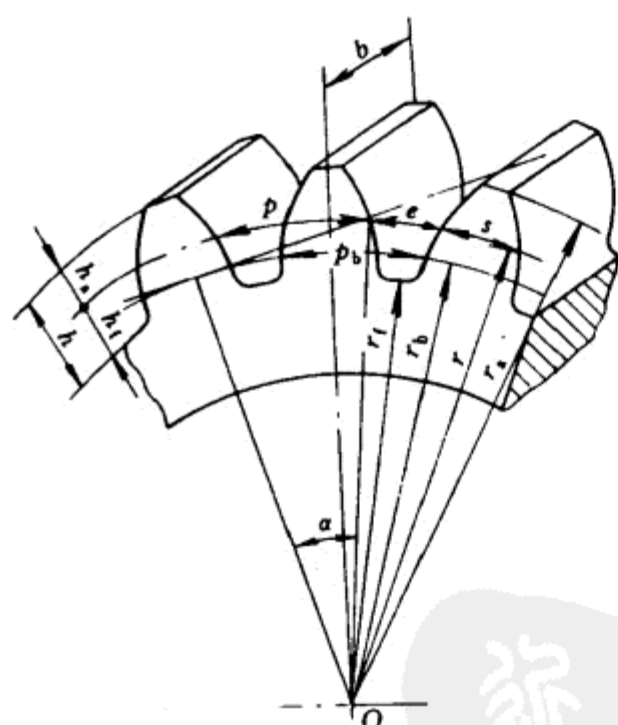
标准直齿圆柱齿轮各部分的名称和符号
